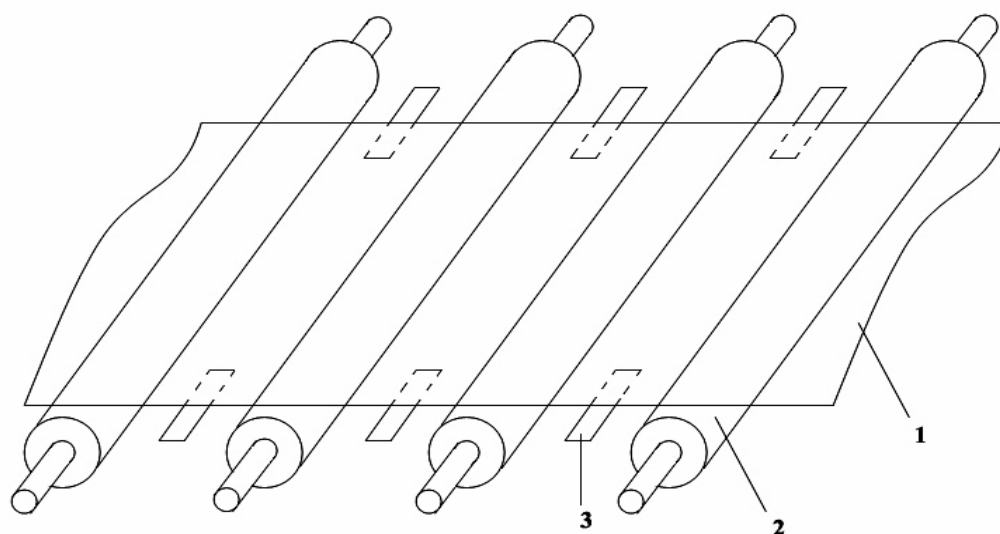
Схема расположения ИК нагревателей в печи отжига (1 зона): 1 – лента стекла; 2 – металлические валы; 3 – ИК нагреватели
